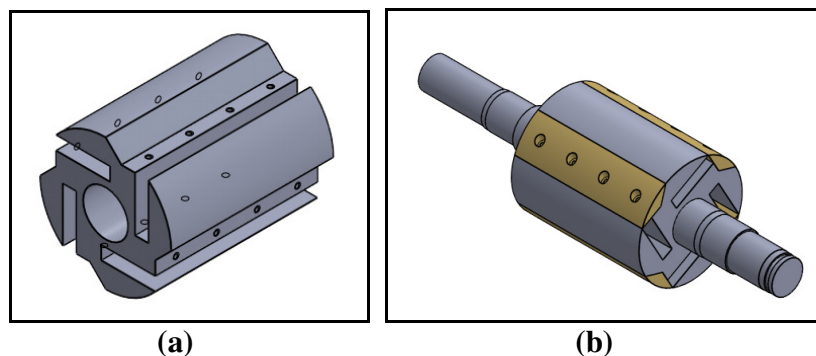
Projeto do Rotor – (a) Detalhe dos sulcos para inserção dos ímãs – (b) Desenho dimensional
